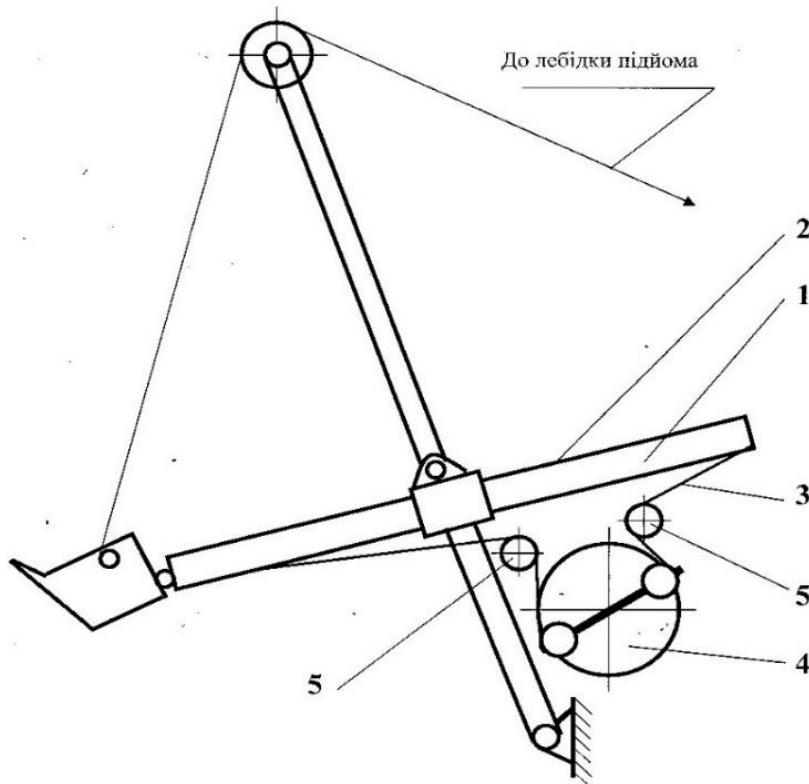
Конструктивна схема механізму натиску ковша екскаватора - прямої механічної лопати.
